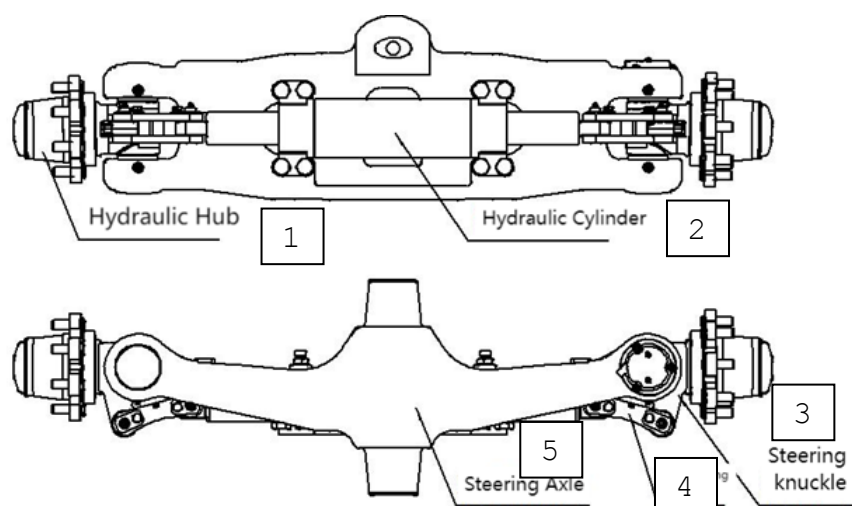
Схема конструкции рулевого моста вилочного погрузчика:
